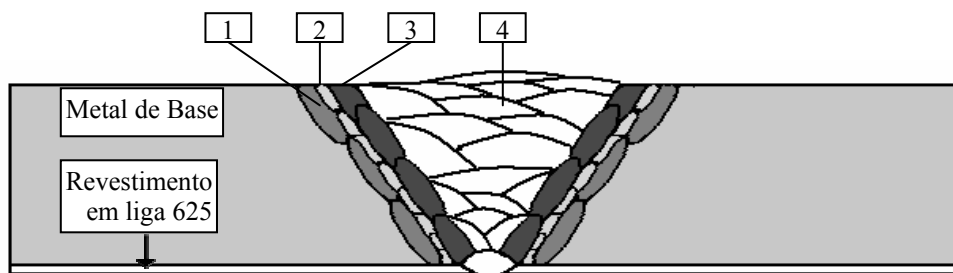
Esquema proposto para execução da soldagem dissimilar em dutos revestidos. Onde: 1) amateigamento com material similar ao metal de base X-60; 2) primeira camada de solda dissimilar (E NiCrMo-3) com a mínima corrente de soldagem possível; 3) segunda camada de E NiCrMo-3 com alta energia de soldagem e 4) soldagem de preenchimento da junta (máxima produtividade).
